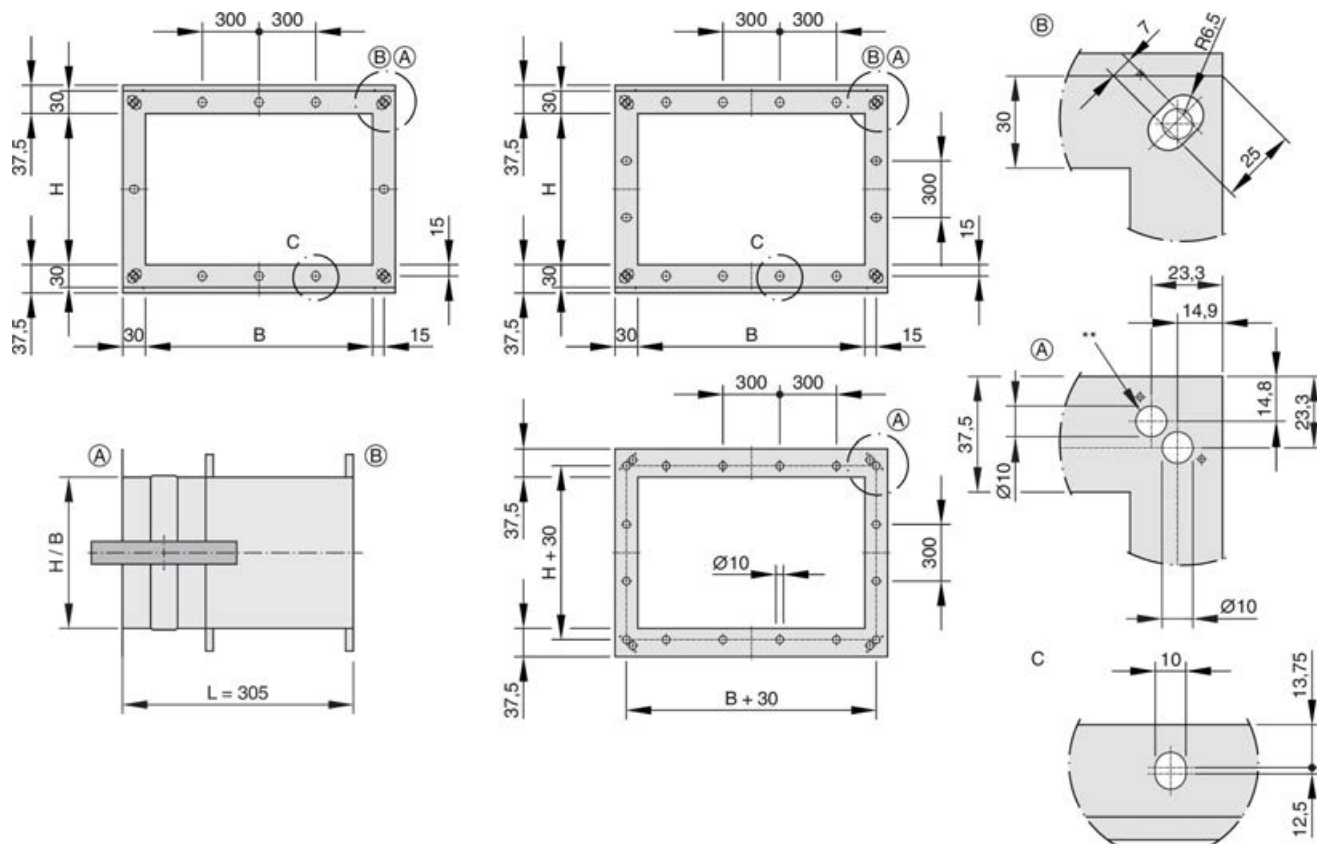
Flangehuller L = 305 mm – ulige og lige antal huller
